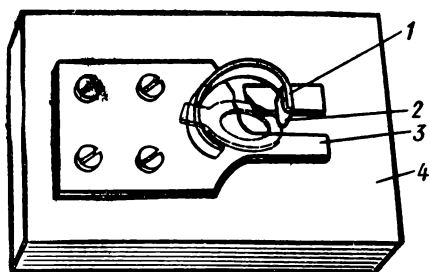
Приспособление для пайки пружин: 1 — пружинодержатель, 2 — пружина, 3 — пластина, 4 — основание
